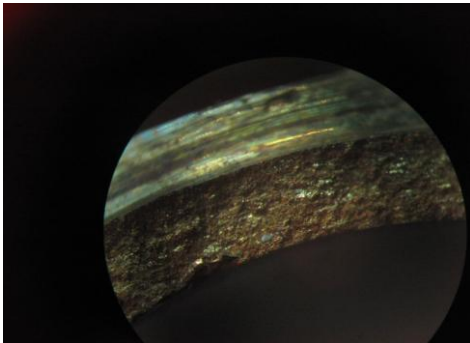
Шлакові і неметалеві включення по поверхні злому корпусу штуцера
